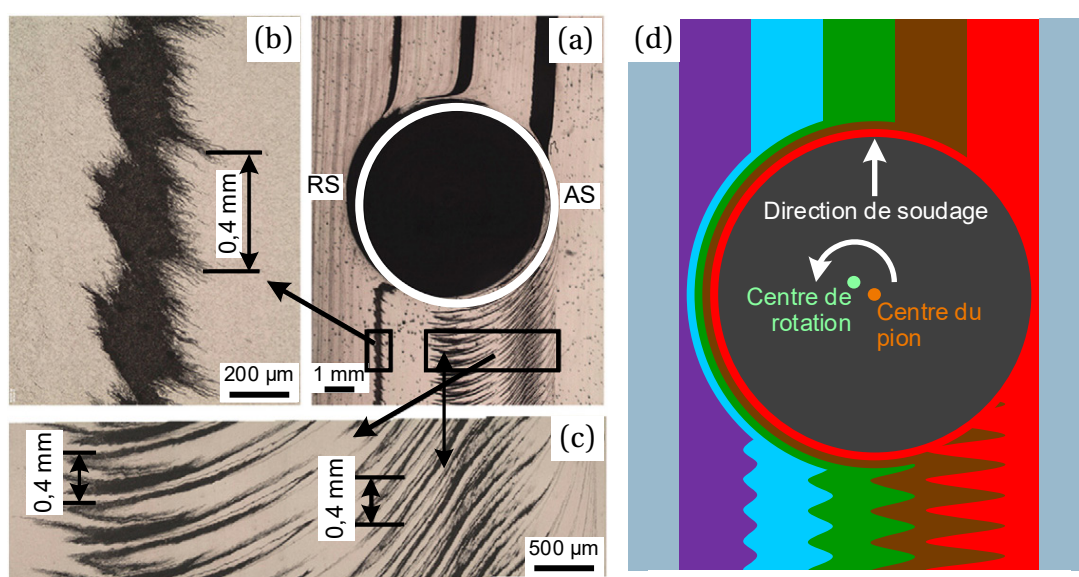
Suivi du flux de matière par marqueur pour le soudage de 304L (a, b et c) vue de dessus globale et de détail à 2 mm de profondeur, (d) schématisation globale [92].
